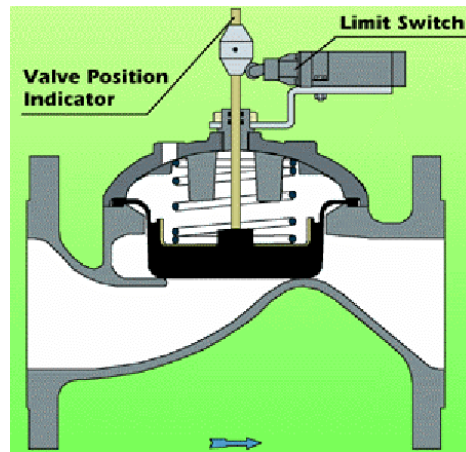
Válvula de asiento equipada con indicador de posición y final de carrera
